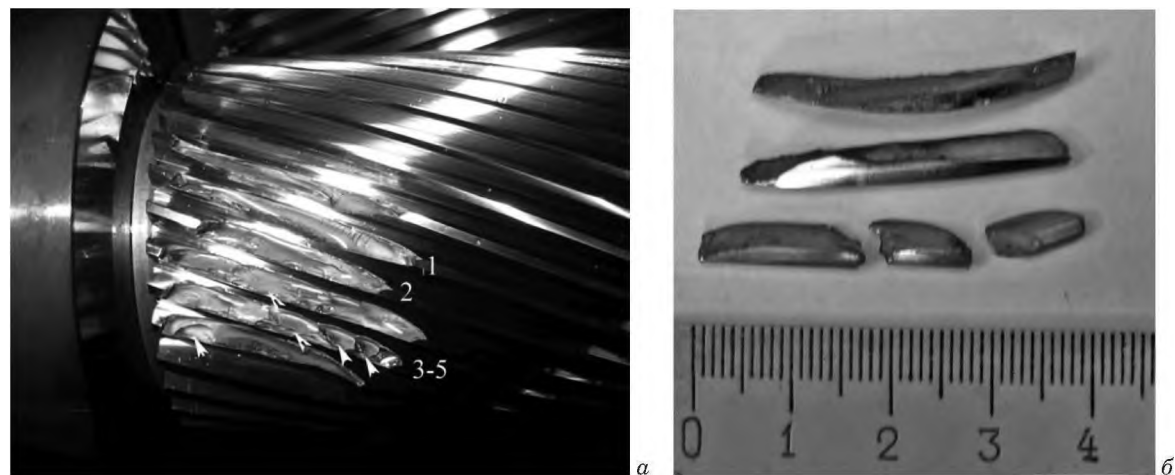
Фотография шестерни с разрушившимися зубьями (стрелками показаны места очаговых усталостных трещин) (а) и фрагменты зубьев, которые были исследованы (б)
